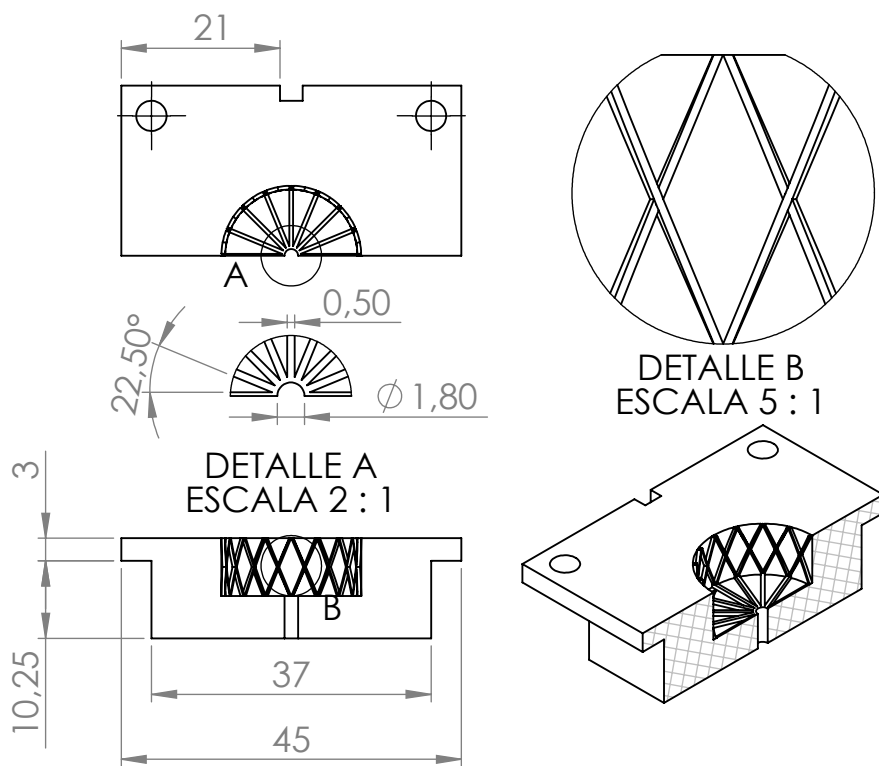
Vista en corte del molde del *Robot Biaxial* parte A
